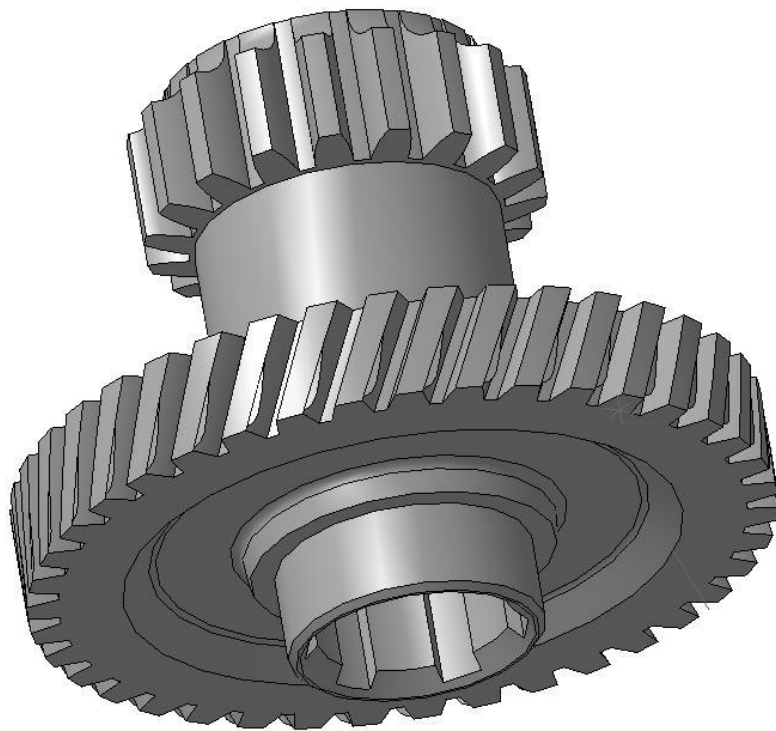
Блок шестерен горизонтально-фрезерного станка
